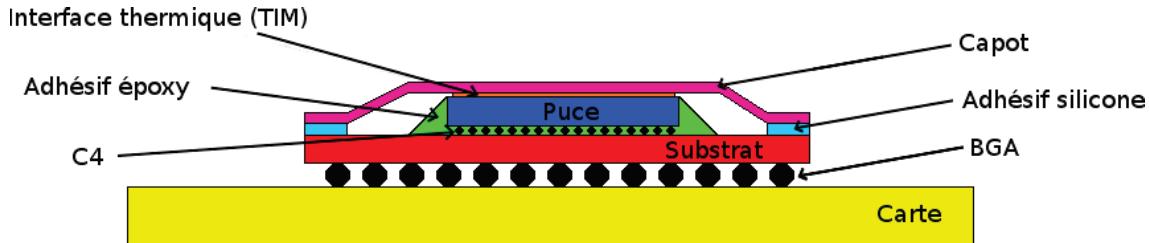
Schéma d'un module FCBGA assemblé sur une carte
